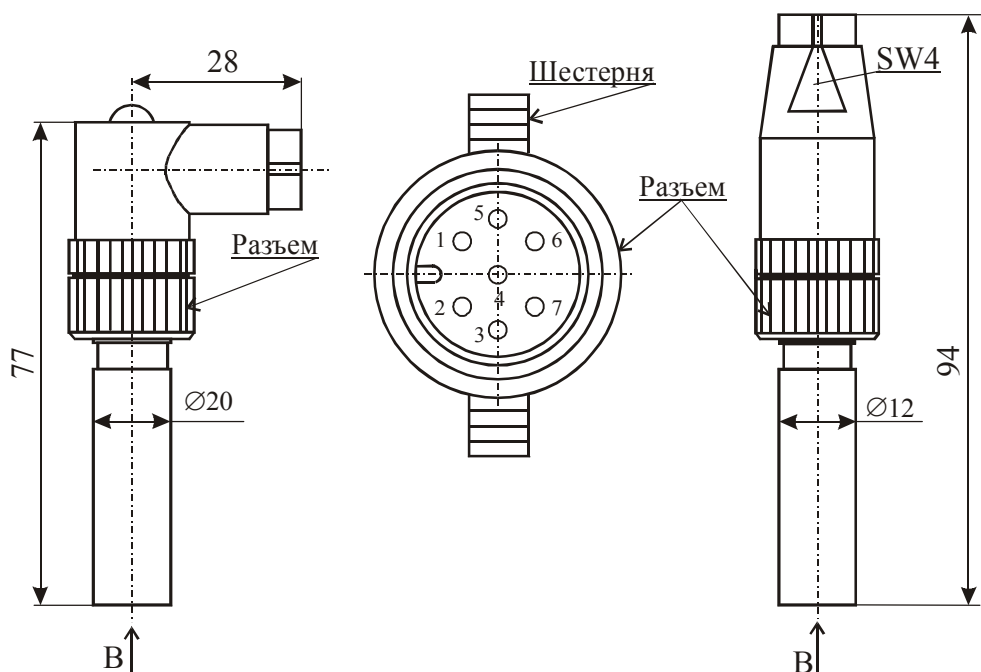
Внешний вид и габаритные размеры датчиков серии GEL 243
